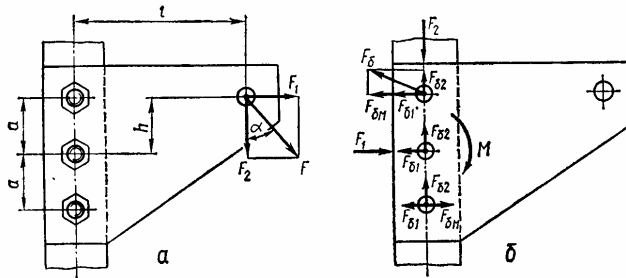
Схема навантаження болтів у кріпленні кронштейна
